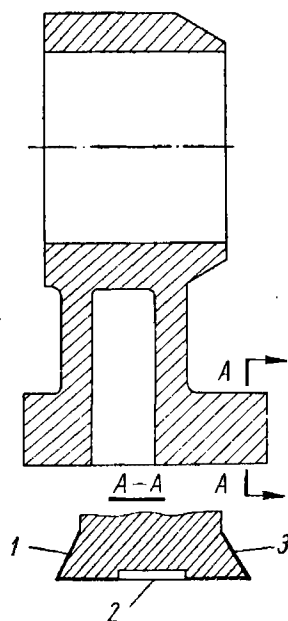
Поддерживающий кронштейн фрезерного шпинделя
